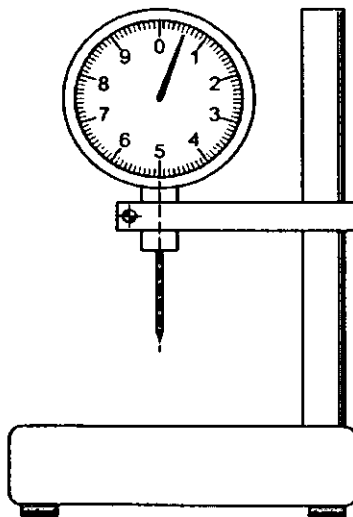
Прилад з рухомим плунжером, закріплений на штативі
